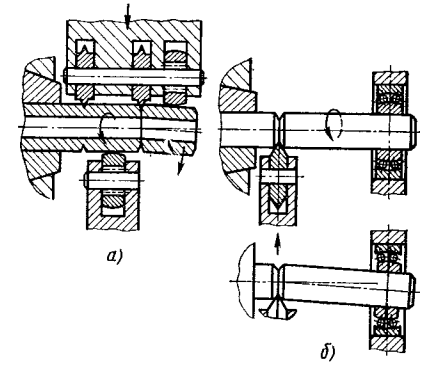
Схемы разделения круглого проката и труб на заготовки обкаткой клиновым роликом (а), обкаткой и разрушением (б)
